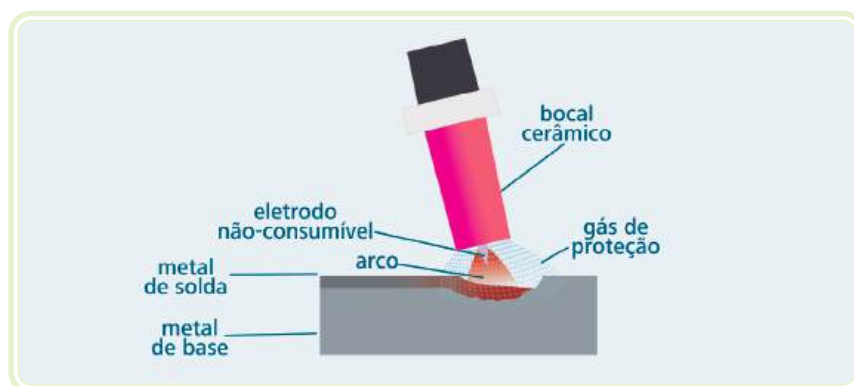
Visão esquemática de uma soldagem TIG apresentando os principais componentes
